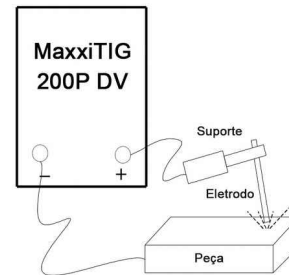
Conexão positiva para soldagem com eletrodo revestido
